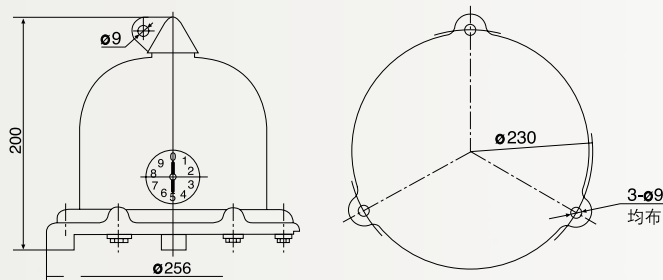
JS-7 放电计数器外形、接线端子及安装尺寸
